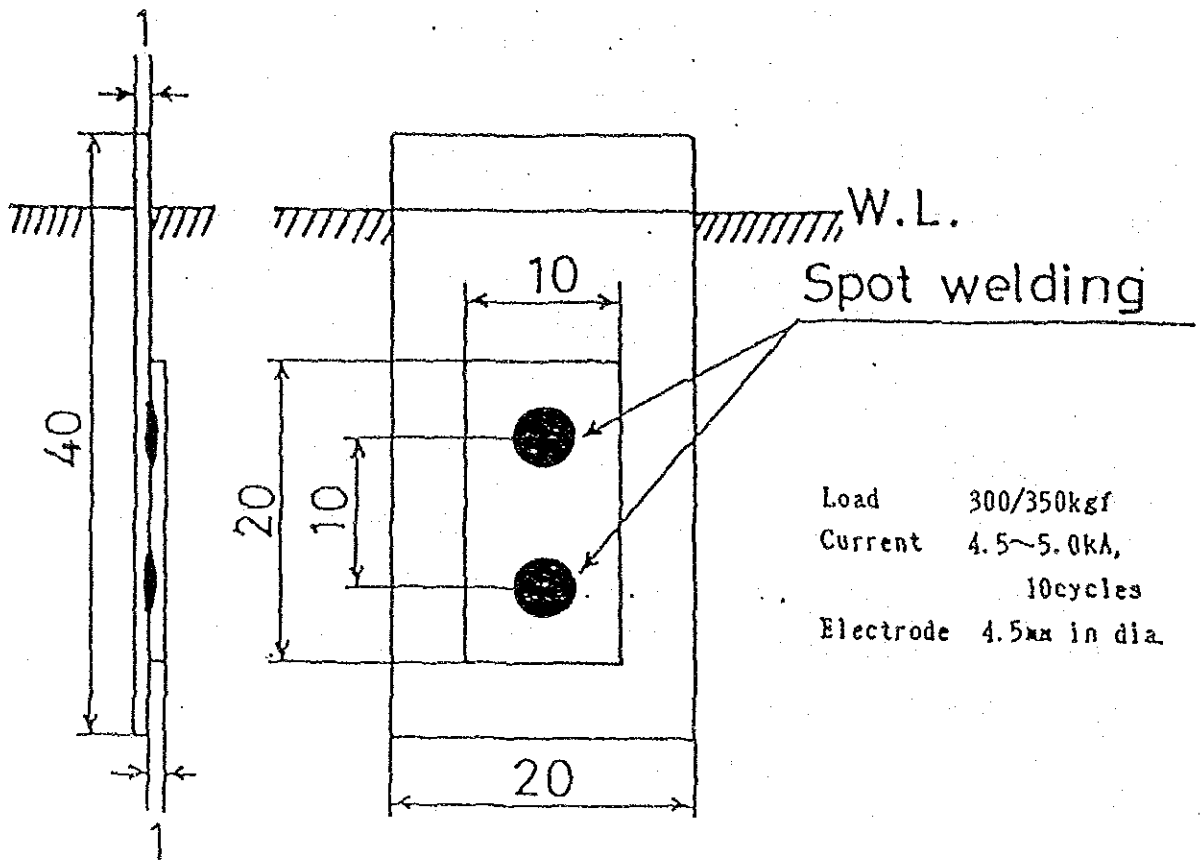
Spot welded specimen for crevice corrosion test. ⁵²⁾
